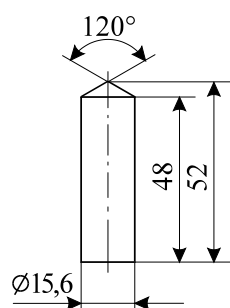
Цилиндрический бронзовый поршень; размеры в мм
